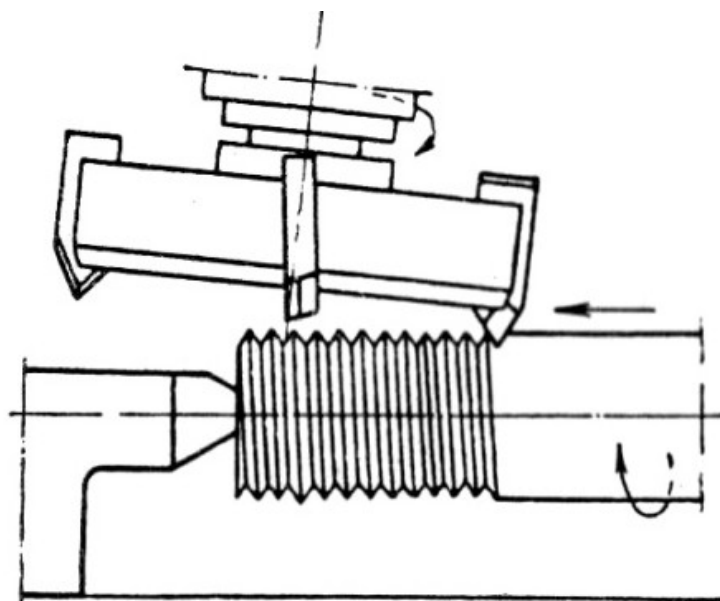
Фрезерование резьбы торцевой фрезой.
